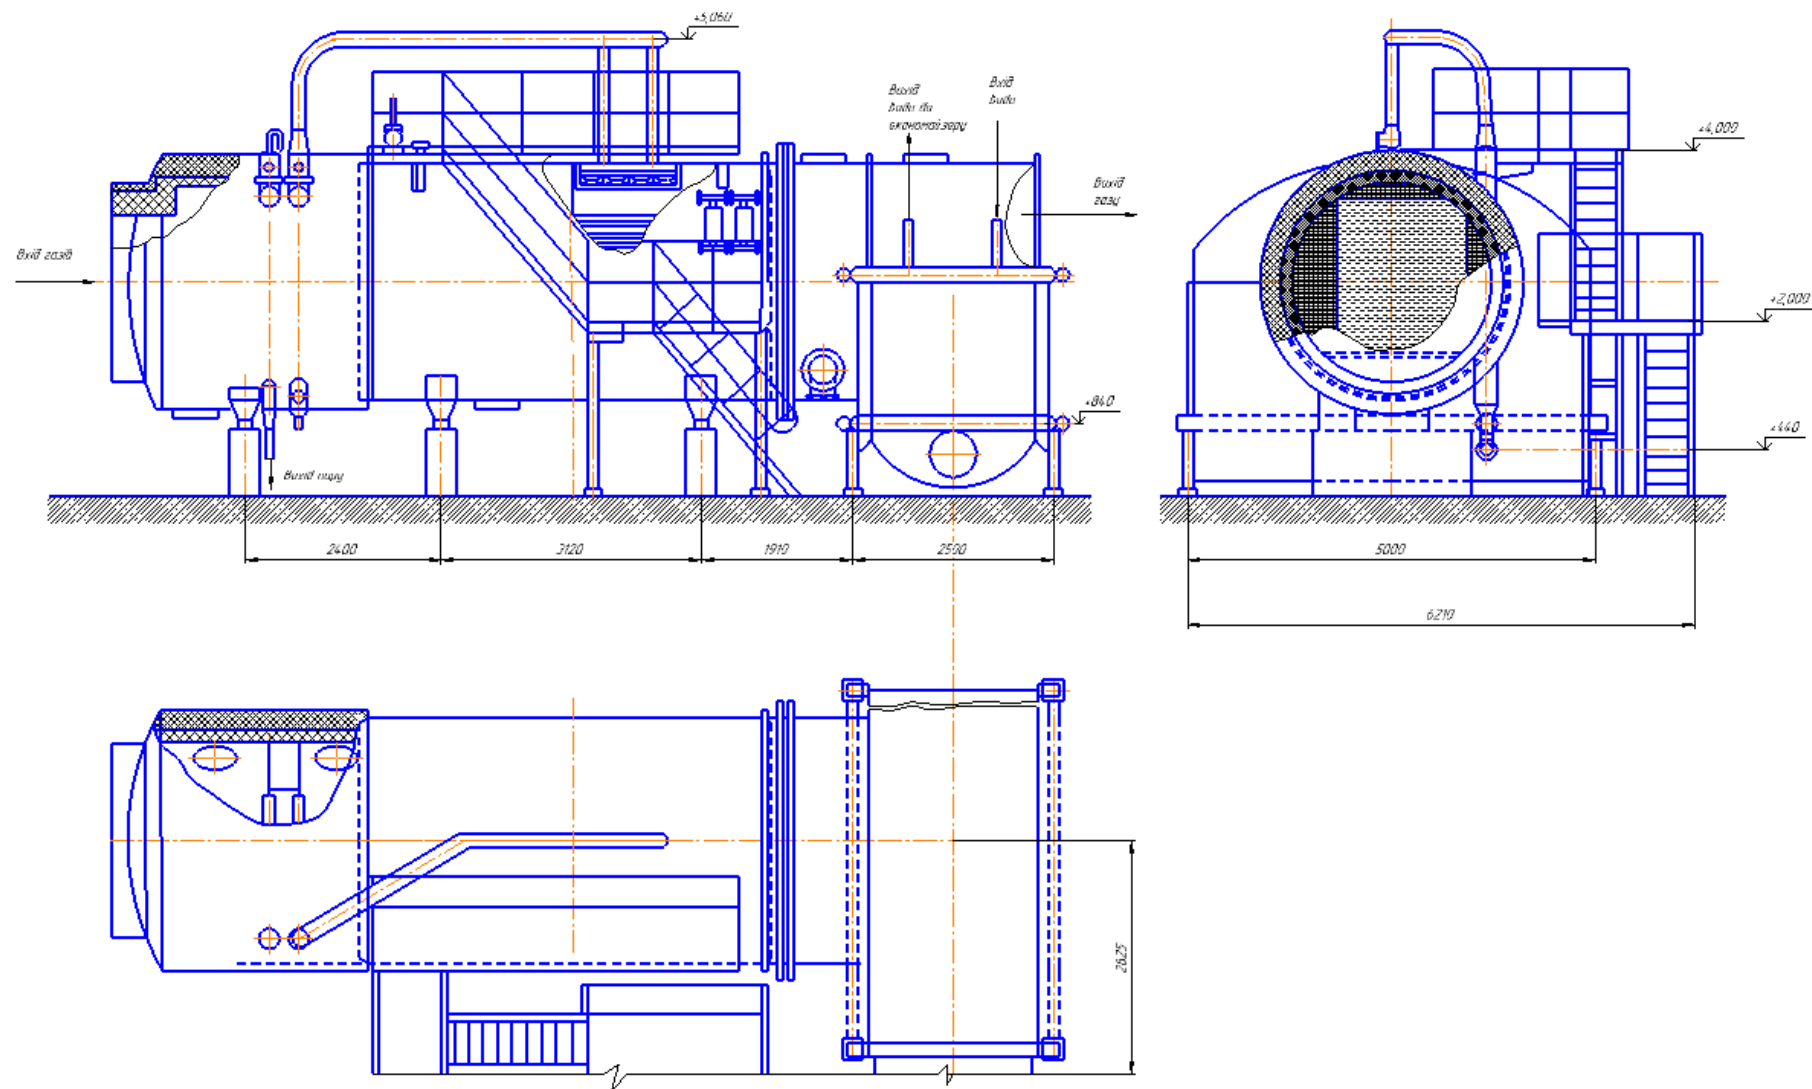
Загальний вигляд котла-утилізатора
